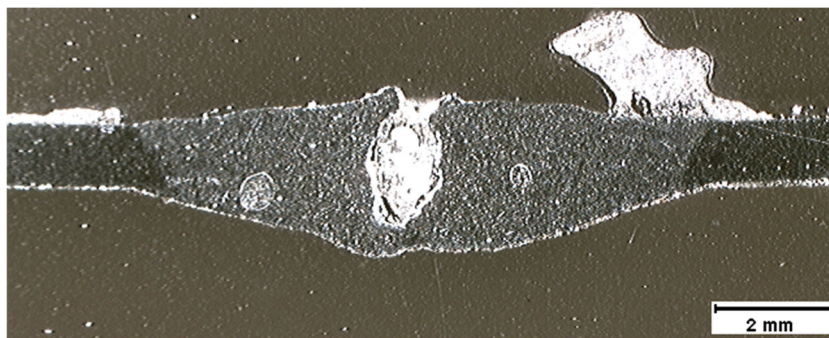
Macrografia (10x) de cordão de solda da classe cratera. Seção transversal M-M do cordão de solda nº 24 – Figura 5.7. Fonte: Autor.
